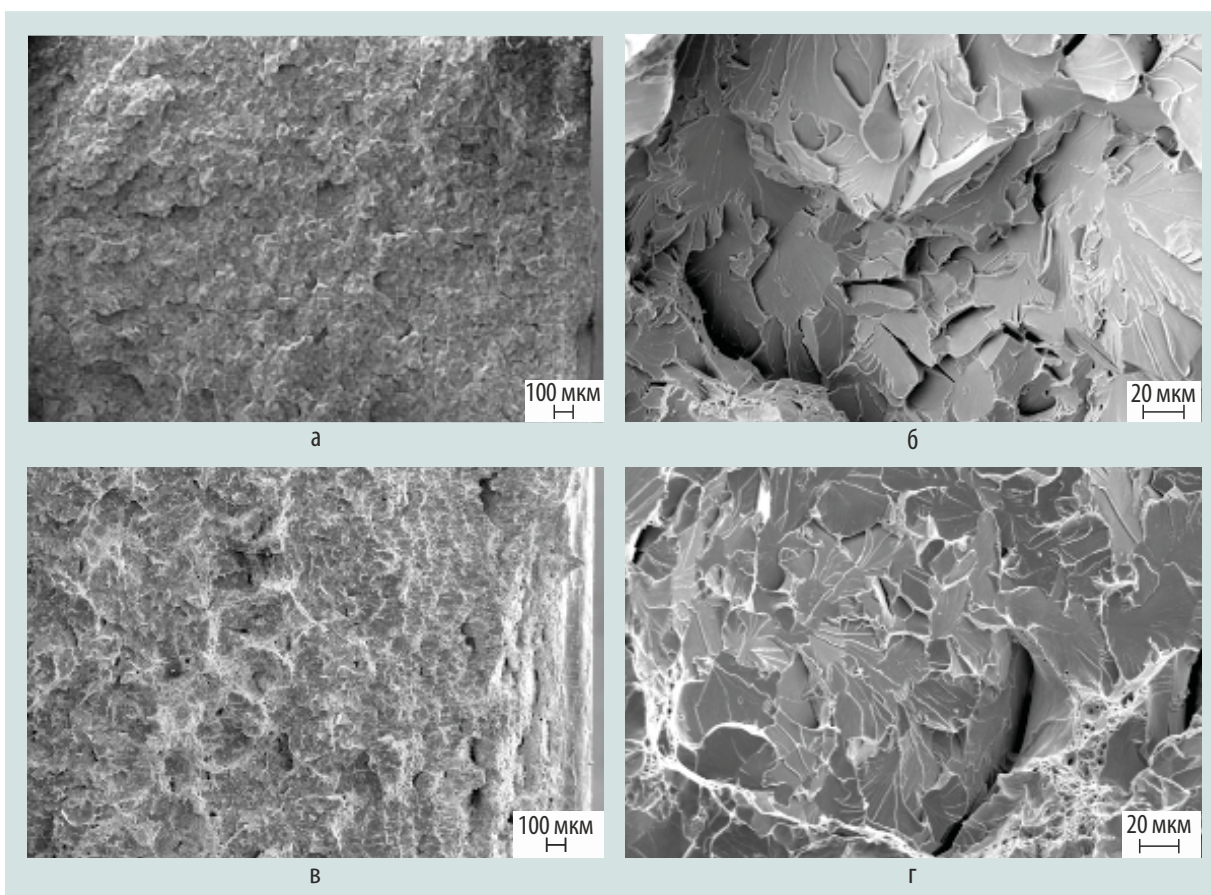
Микроструктура поверхности разрушения образцов корпуса пароперегревателя (а, б) и испарителя (в, г) после испытаний на ударный изгиб при температуре испытаний 20 °С
